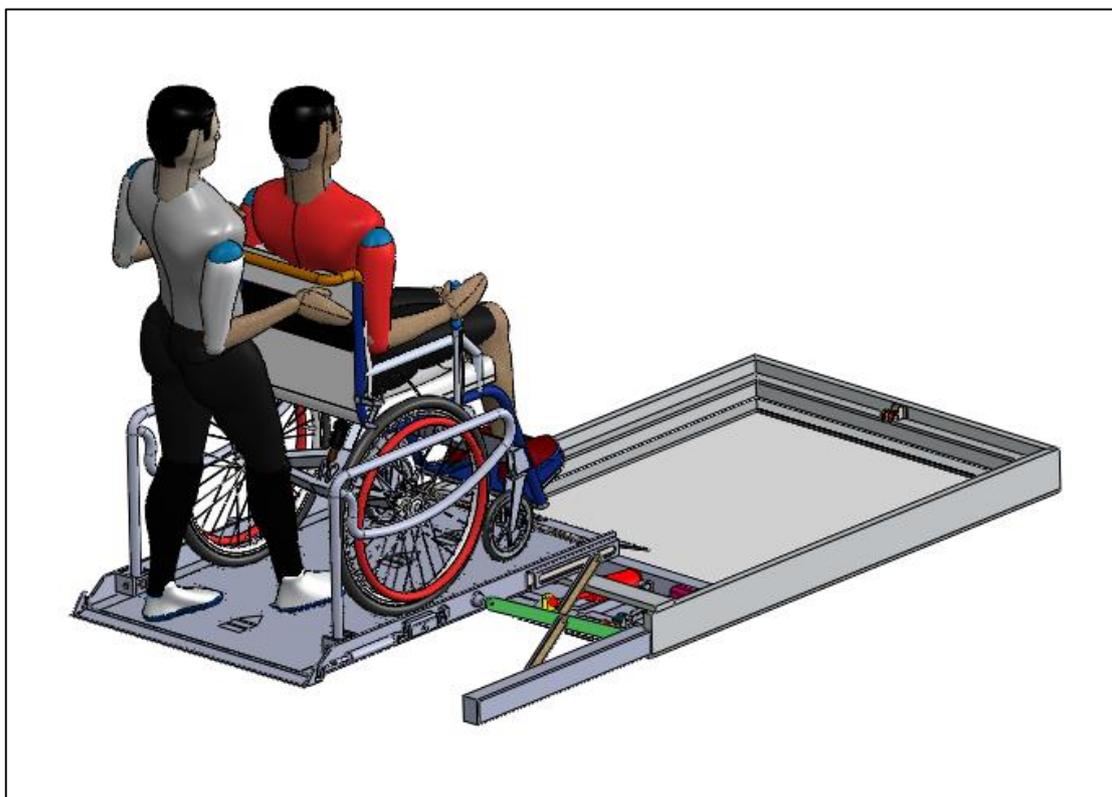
Disposition du PMR à la plateforme- vue face et arrière -
